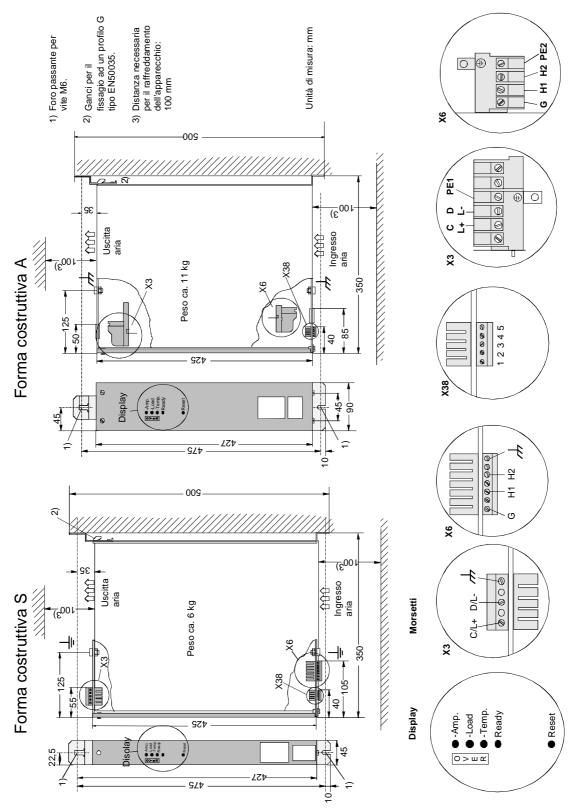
Dimensioni di ingombro per forme costruttive S e A
